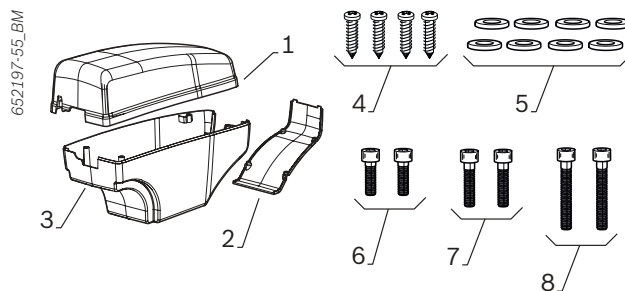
Accesorios para el montaje de la cubierta trasera de la columna
